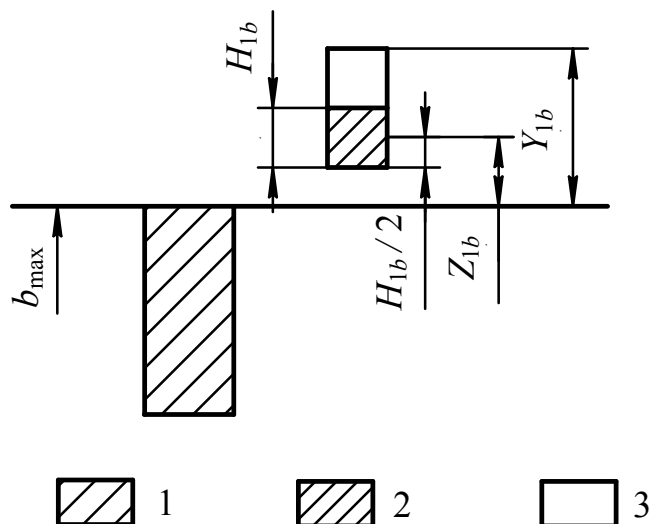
Поля допусків: 1 - розміру b вала; 2 - калібра-кільця; 3 - поле зносу калібра-кільця на виготовлення
